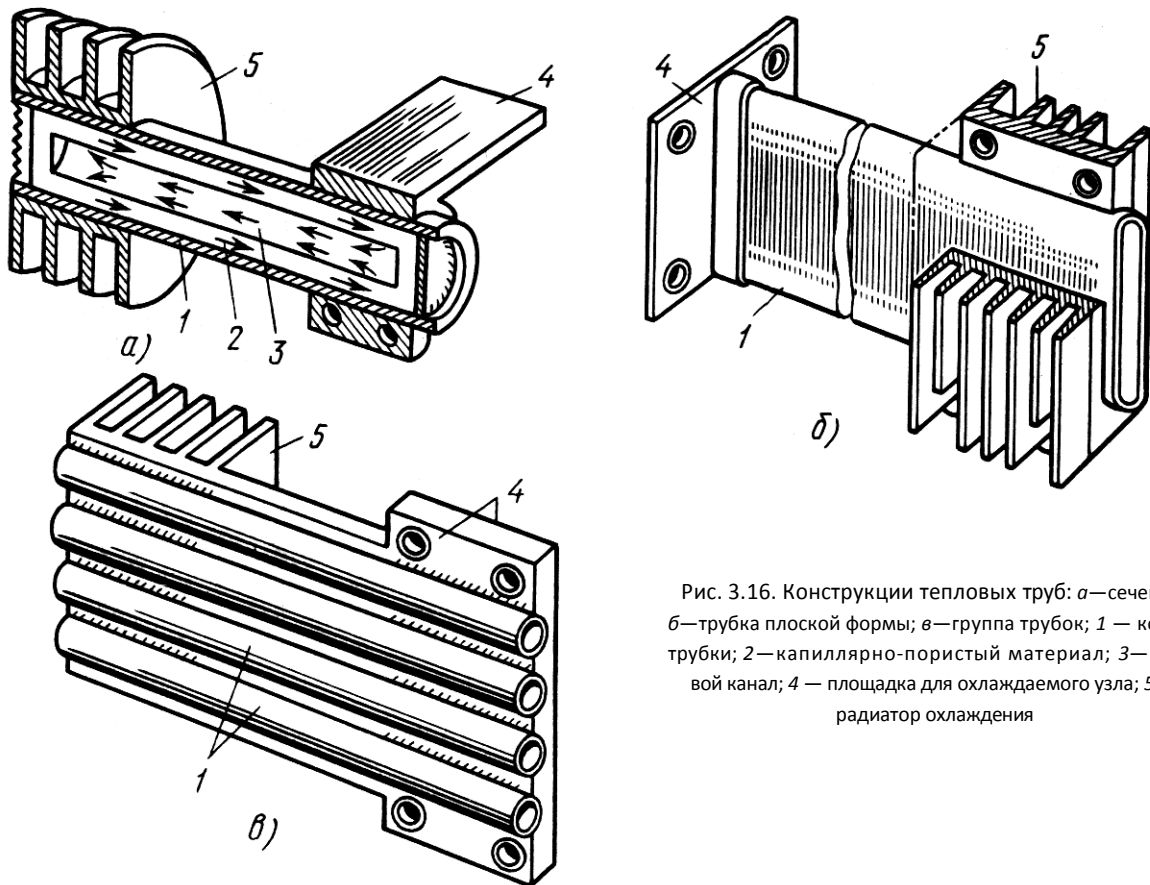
Конструкции тепловых труб: а—сечение; б—трубка плоской формы; в—группа трубок; 1 — корпус трубки; 2—капиллярно-пористый материал; 3—паровой канал; 4 — площадка для охлаждаемого узла; 5 — радиатор охлаждения
